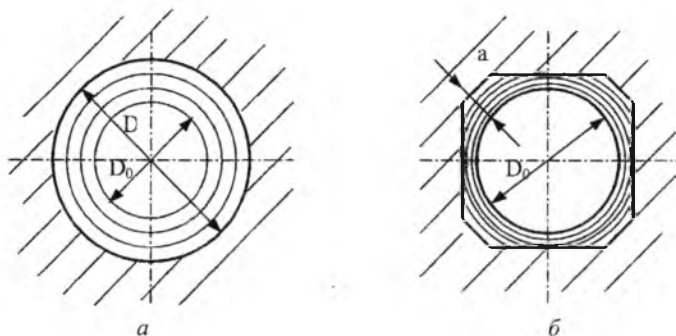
Схема протягивания: а – форма режущих кромок протяжки соответствует профилю обрабатываемой поверхности. Зубья протяжки срезают заданный припуск последовательно, при этом окончательная форма и размеры образуются последним зубом; б – форма режущих зубьев не соответствует профилю обрабатываемых поверхностей. Например, здесь зубья имеют форму дуг окружностей
